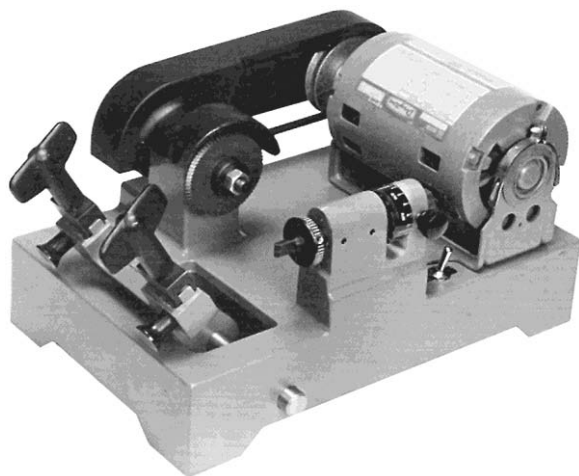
Станок Framon DC-300 сконструирован для нарезания автомобильных ключей по коду и для изготовления их дубликатов (С разрешения компании Framon Manufacturing Co., Inc.)
